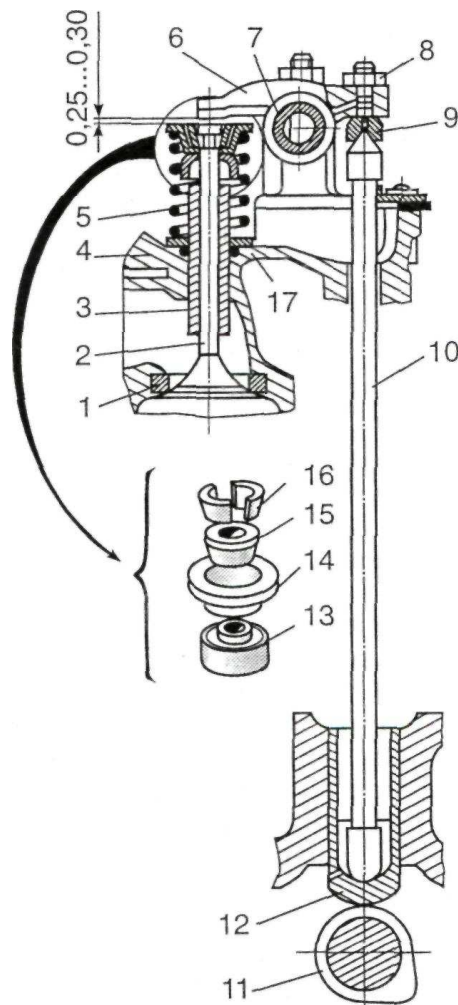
Механізм газорозподілу двигунів з нижнім розташуванням розподільного вала та верхнім — клапанів:
